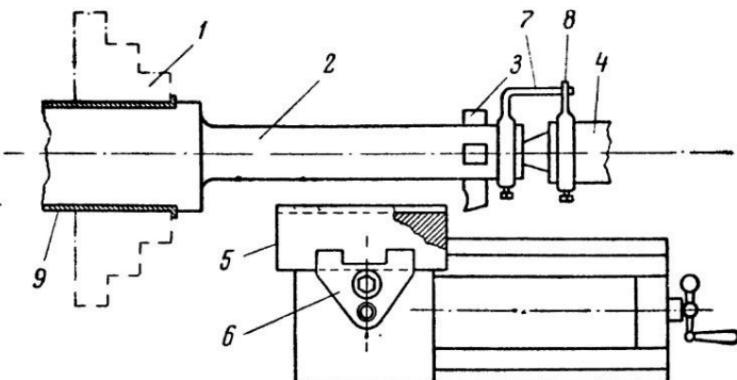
Строгание канавки на токарном станке: 1 — кулачки патрона; 2 — державка; 3 — резец; 4 — пиноль задней бабки; 5 — обрабатываемая деталь; 6 — планка резцедержателя; 7 — хомутик с поводком; 8 — хомутик; 9 — втулка-оправка.
